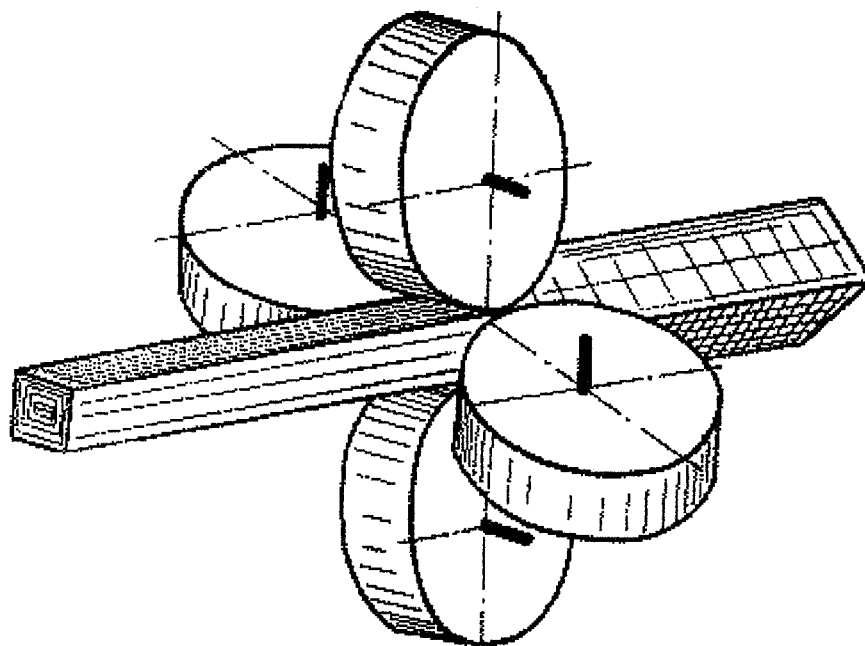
Схема прокатки квадратной полосы в четырехвалковом калибре
